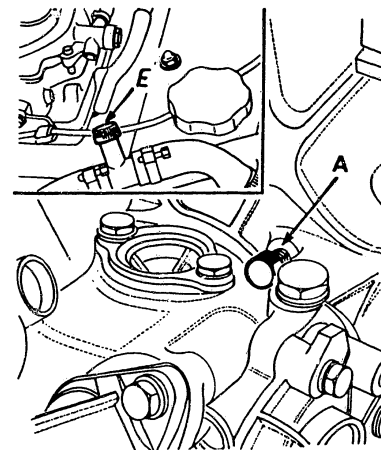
A bezeichnet den Kühlmittel-Ablasszapfen im Motorblock, E die Entlüfterschraube (oben links).
